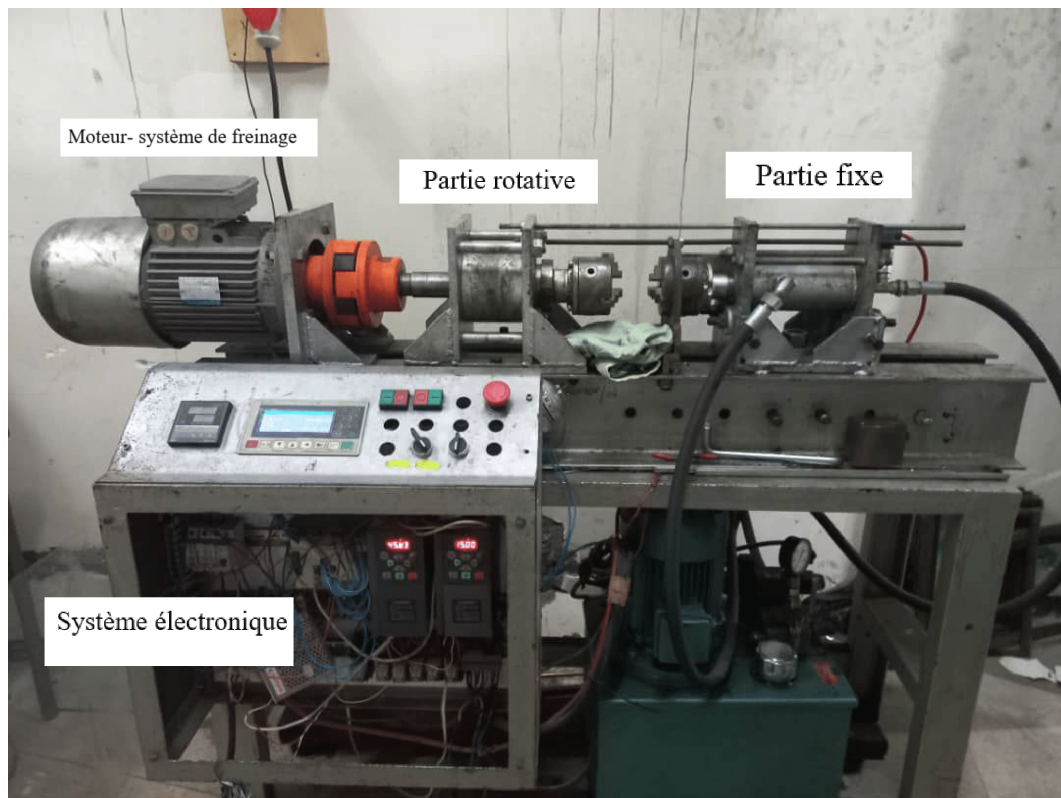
Machine de soudage par friction rotative à entraînement direct
